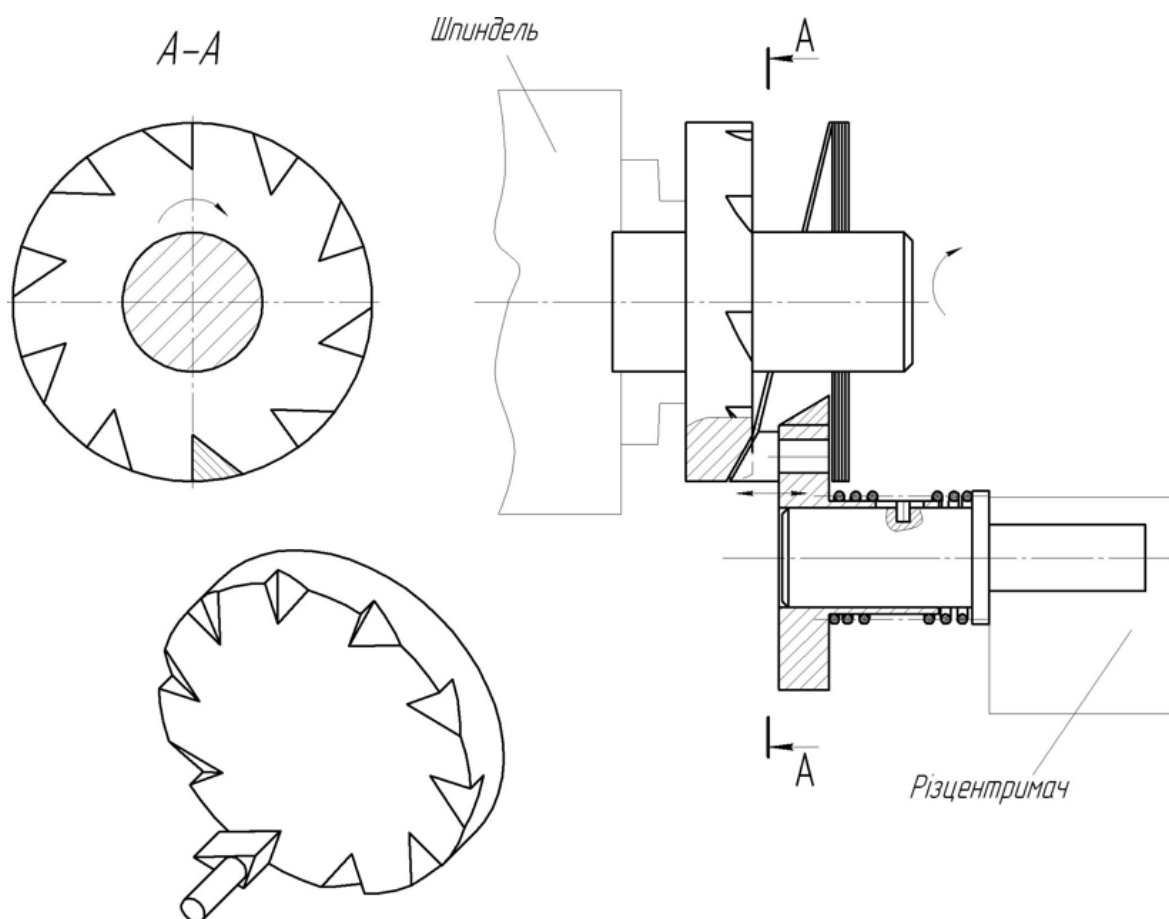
Конструктивна схема способу виготовлення лопатей на шнековій спіралі
